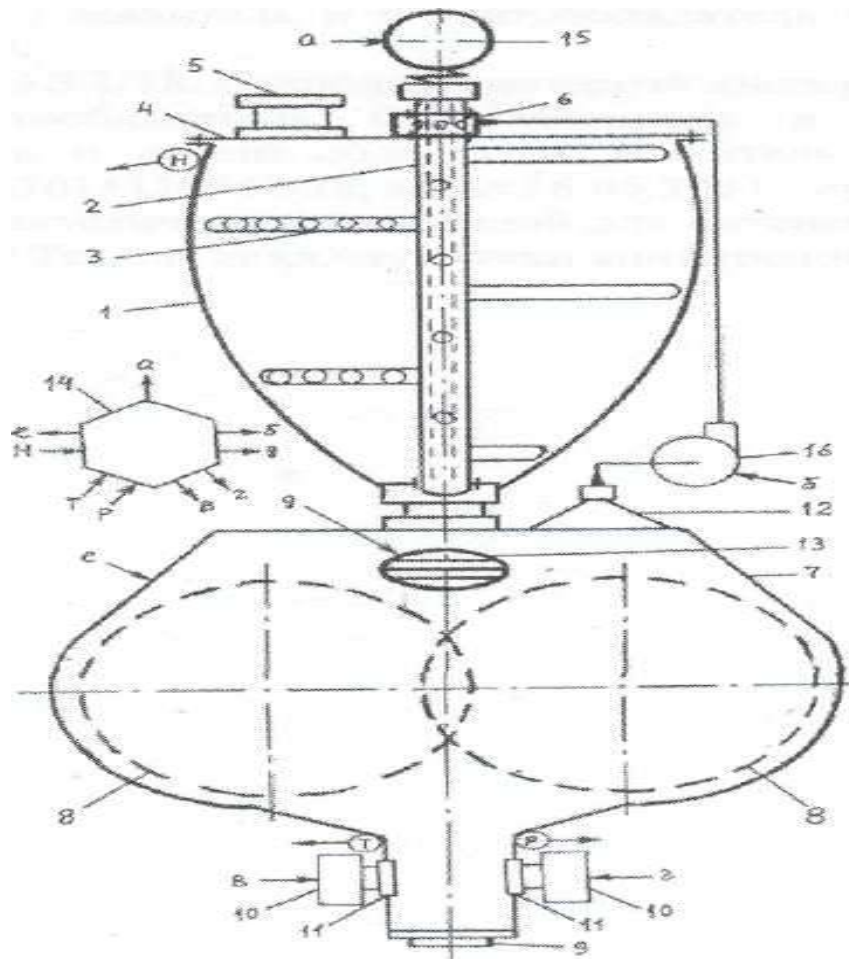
Валково-шестеренный экструдер [37]
